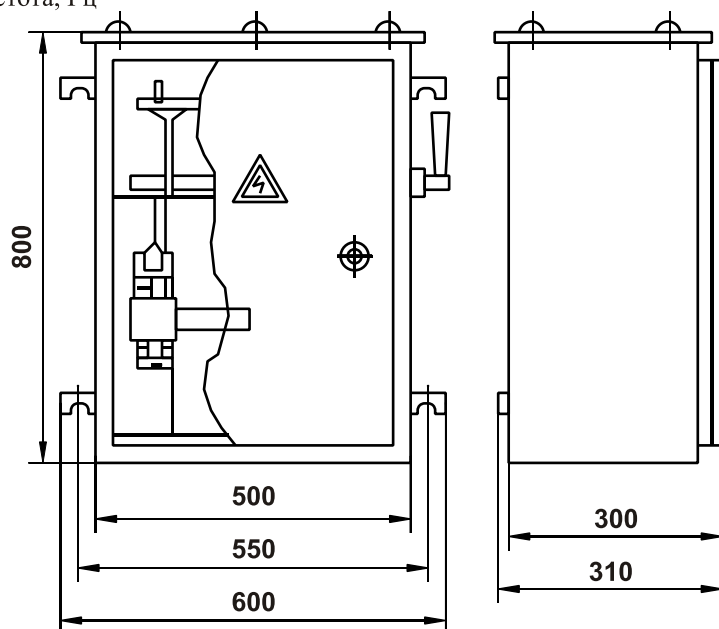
Внешний вид и габаритные размеры ЯВП
